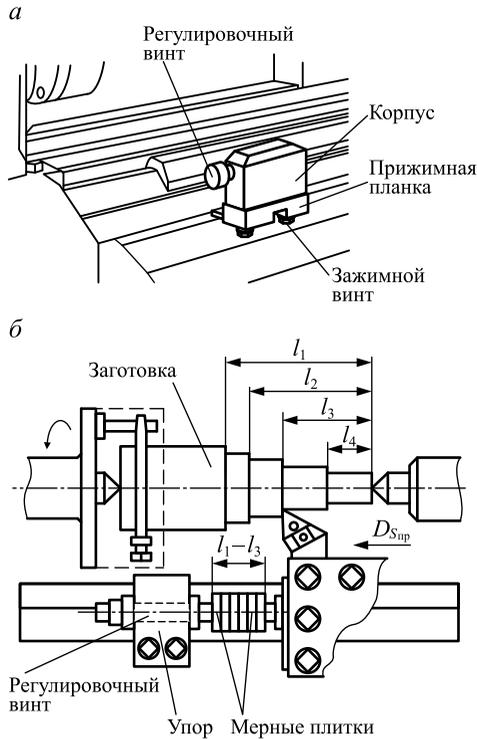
Продольный упор и обтачивание ступенчатого вала с его помощью
